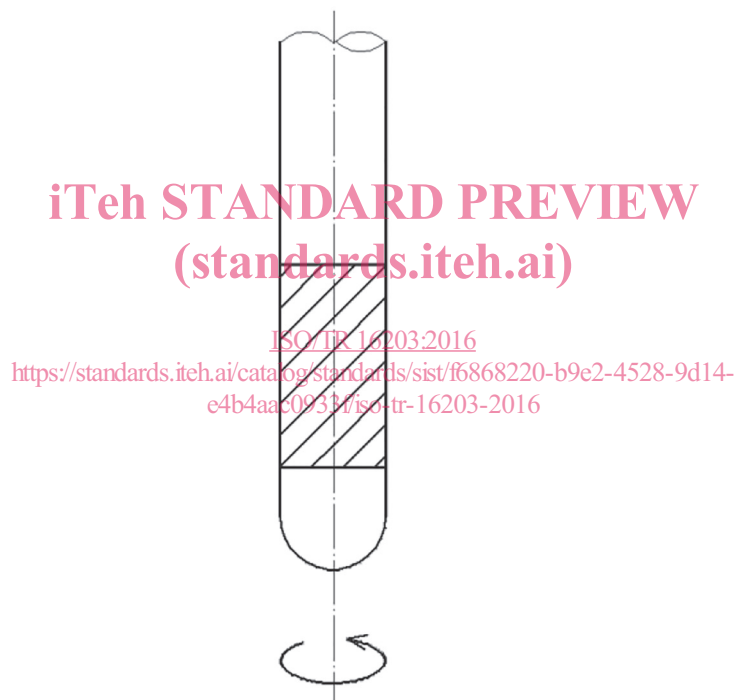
Éprouvette pour essai sur cylindre rotatif
